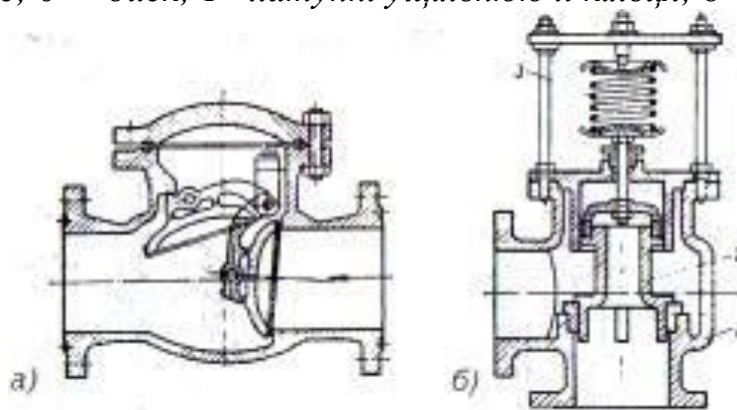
Клапани: а — зворотний; б — запобіжний; 1 — корпус; 2 — клапан; 3 — пружина
